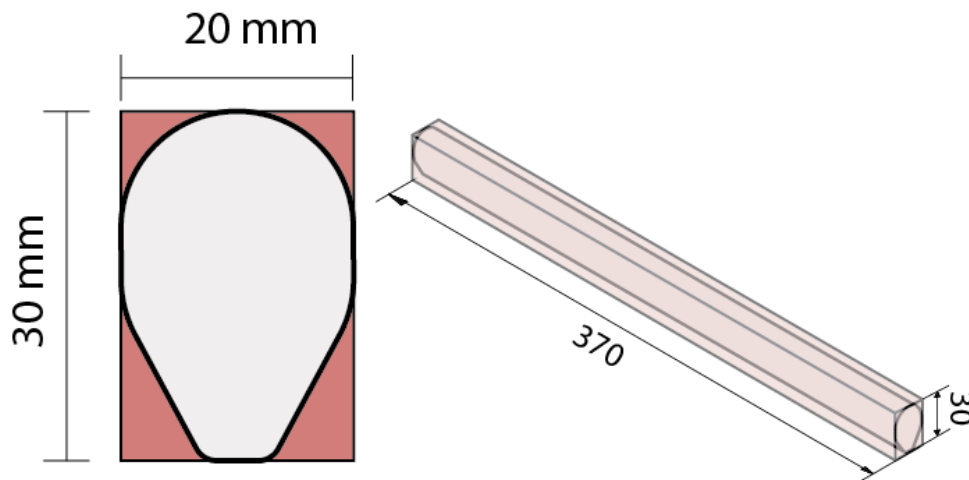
Dimensiones y desbaste del soporte de agarre del separador para corte en plancha de grilon
